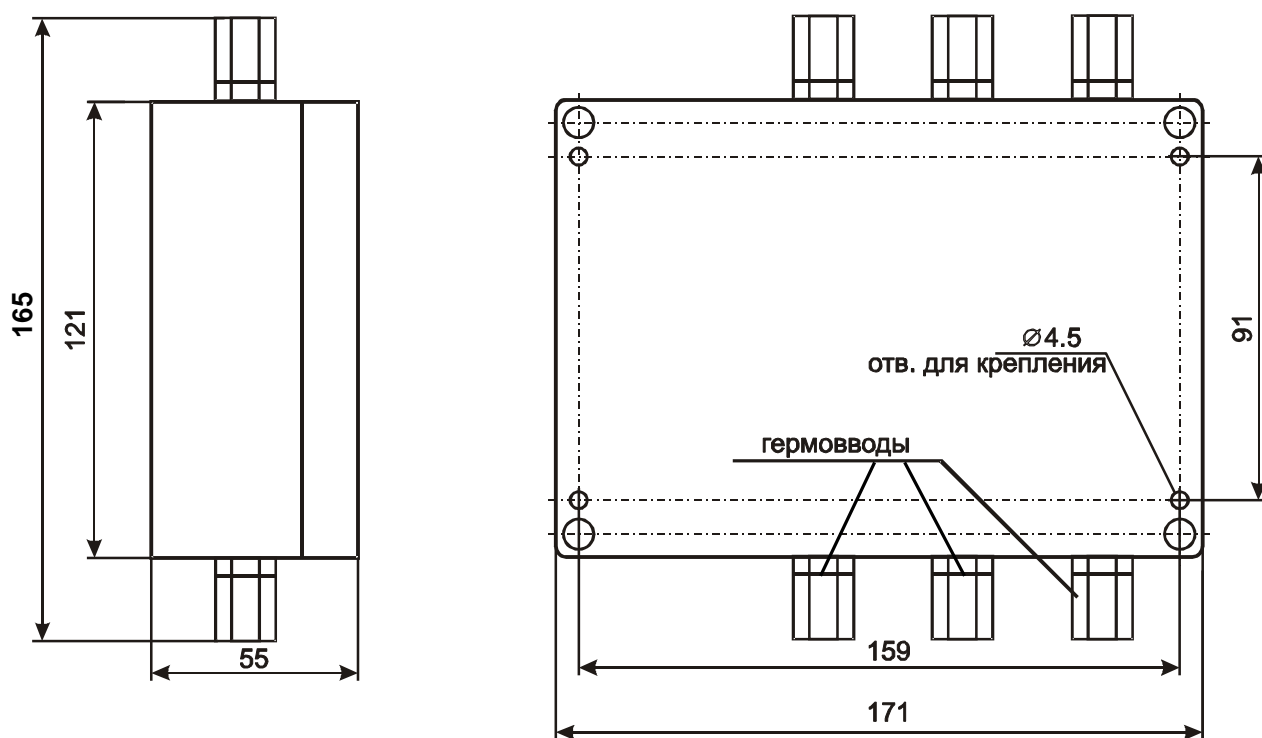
Внешний вид и габаритные размеры СК-01 в исп. IP65
